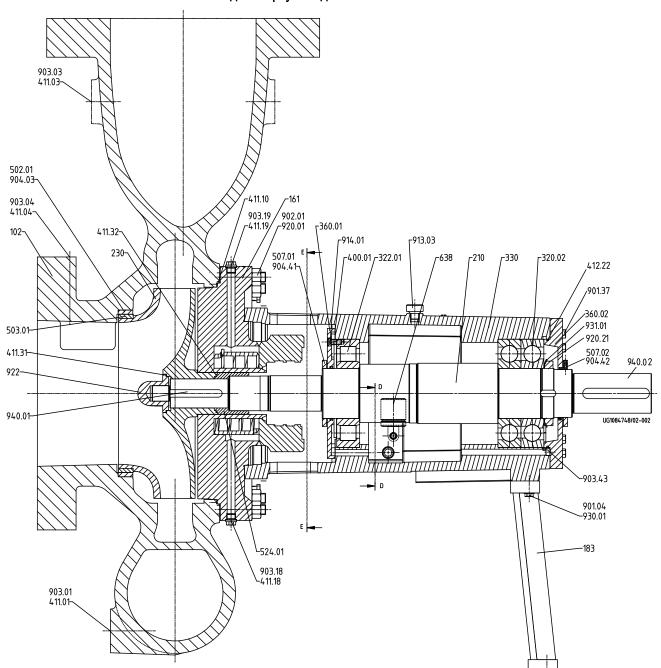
Общий чертеж модели с корпусом подшипника В07
